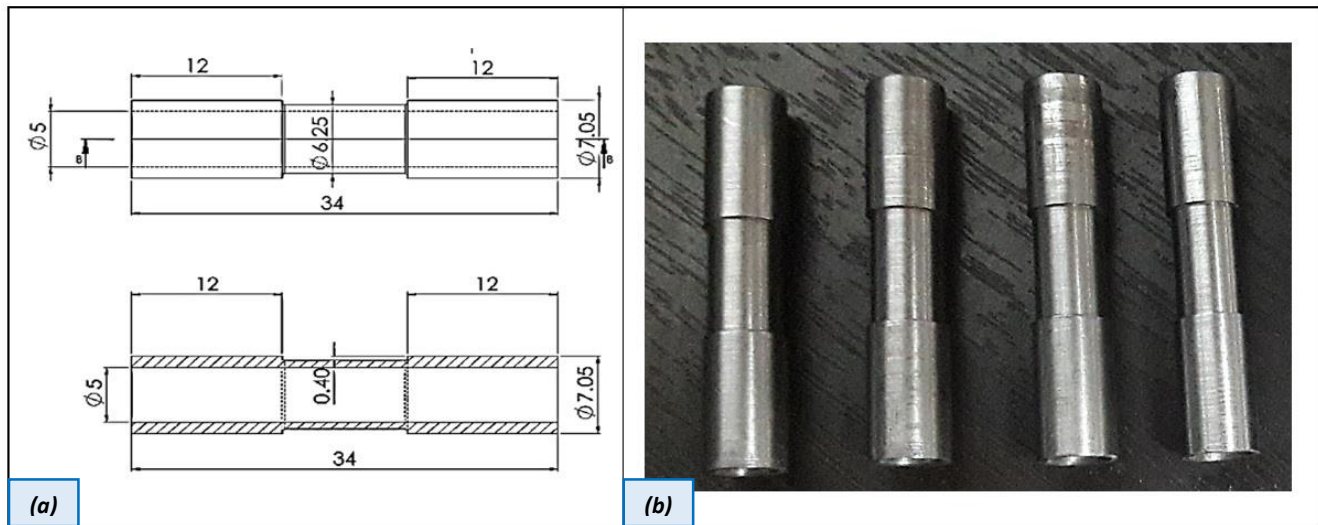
Probeta para dilatometría. (a) Diseño (dimensiones en mm), (b) piezas maquinadas.
